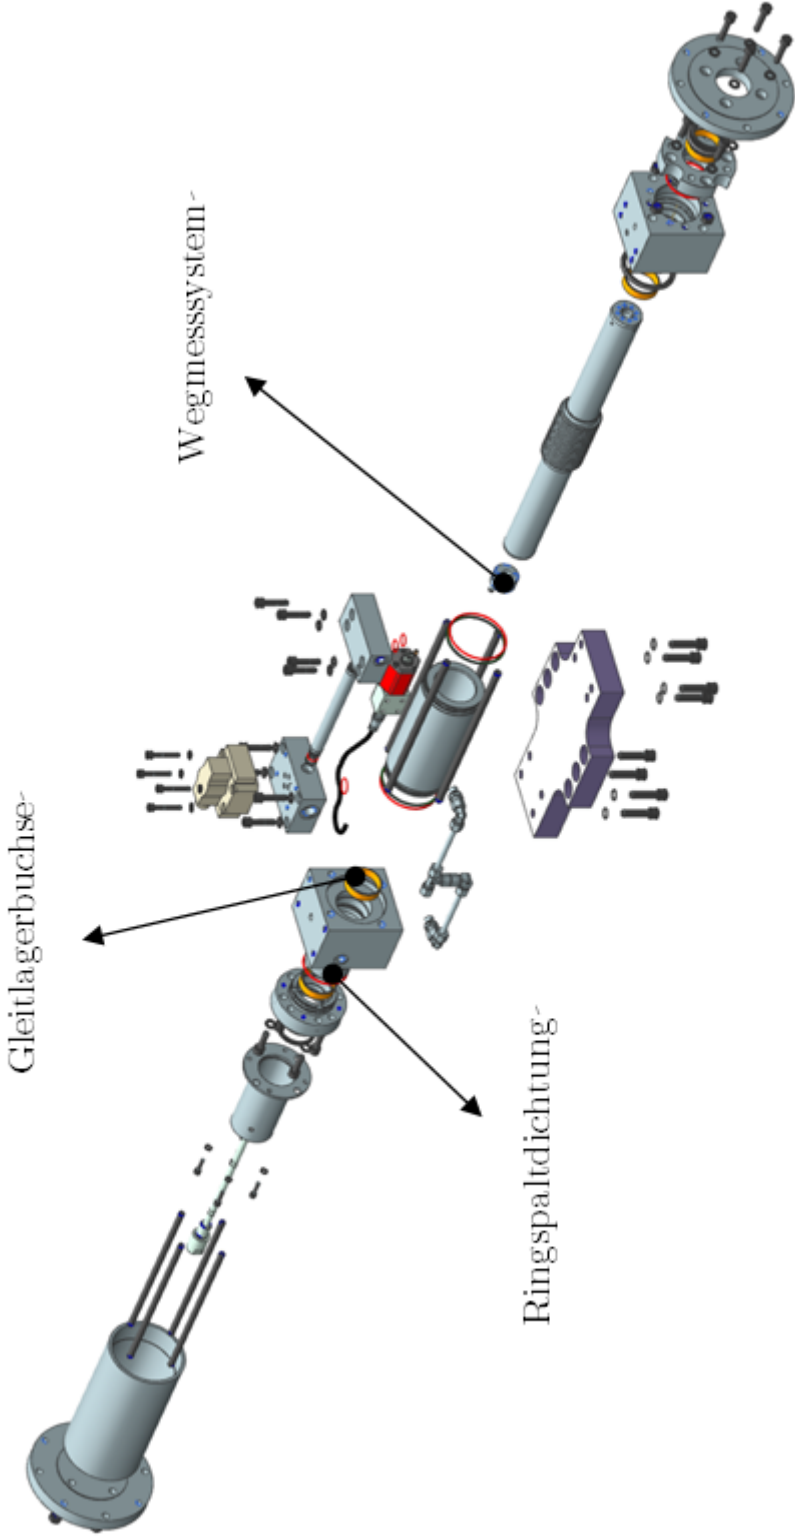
Explosionsansicht des Hydraulikzylinders
